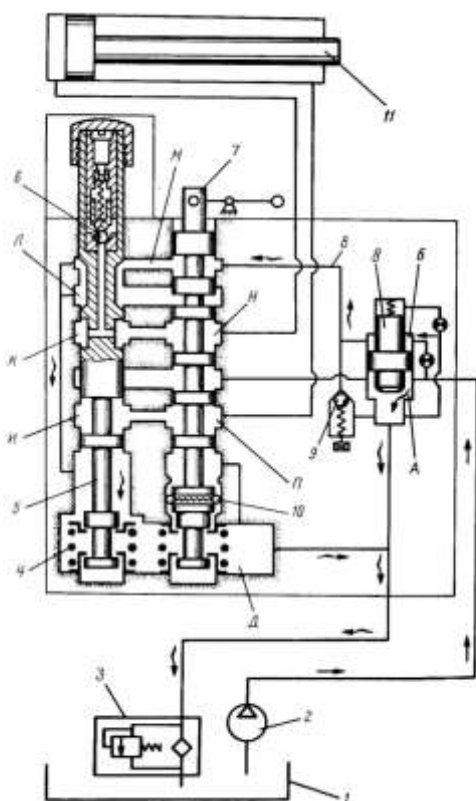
Нейтральное положение золотника: 1 – бак гидросистемы; 2 – шестеренный насос; 3 – фильтр; 4 – пружина; 5 – перегрузочный клапан; 6 – шарик; 7 – золотник; 8 – перепускной клапан; 9 – предохранительный клапан; 10 – шарик-фиксатор; 11 – гидроцилиндр
